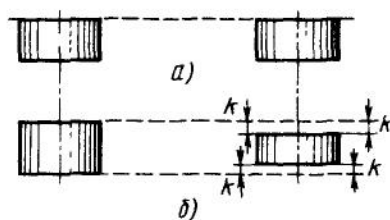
Проверка установки шкивов: а — одинаковой ширины, б — различной ширины
